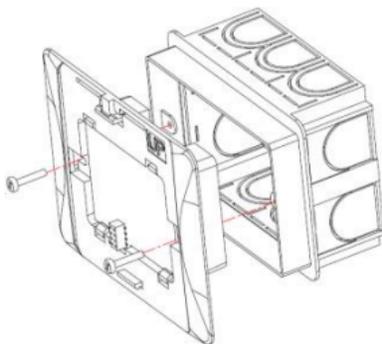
Collegamento placchetta di fissaggio a scatola 503.
